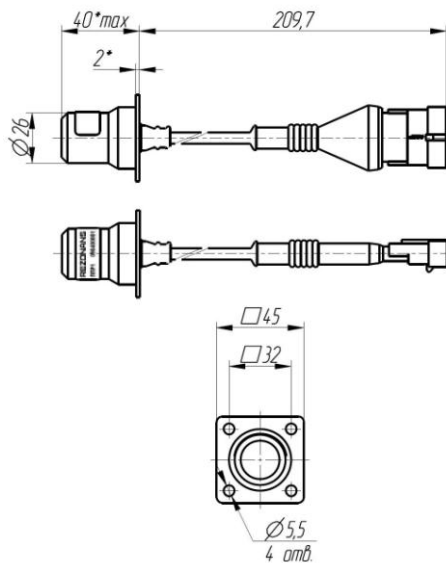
Габаритные и присоединительные размеры ППР1
